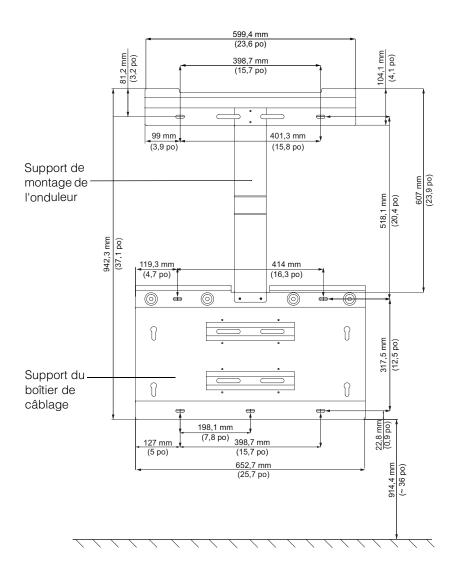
Encombrement des supports de montage – Boîtier de câblage et onduleur
